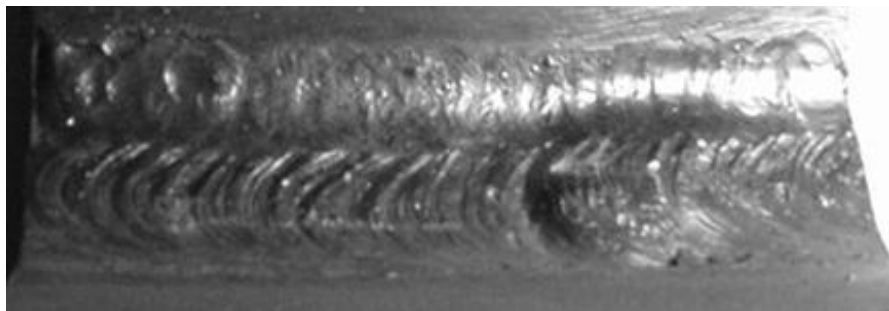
Cordão de soldadura dos provetes da série TDR.
